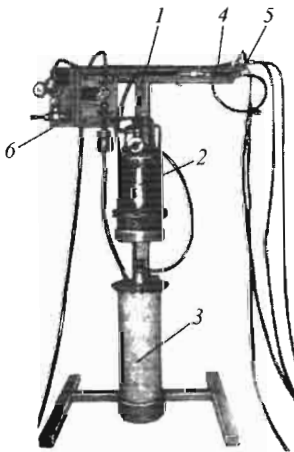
Установка УГФ-90 для газоплюсовой сварки и пайки:
